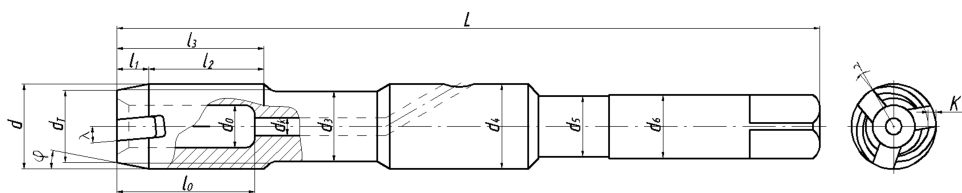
Конструктивные элементы метчика с внутренним размещением стружки
